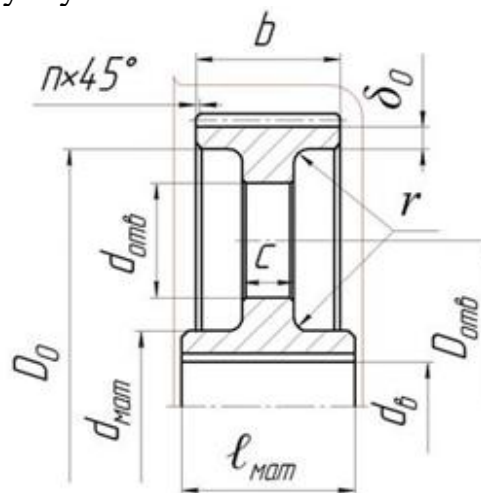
Конструкція циліндричного зубчастого колеса з $d_a < 600$ мм
